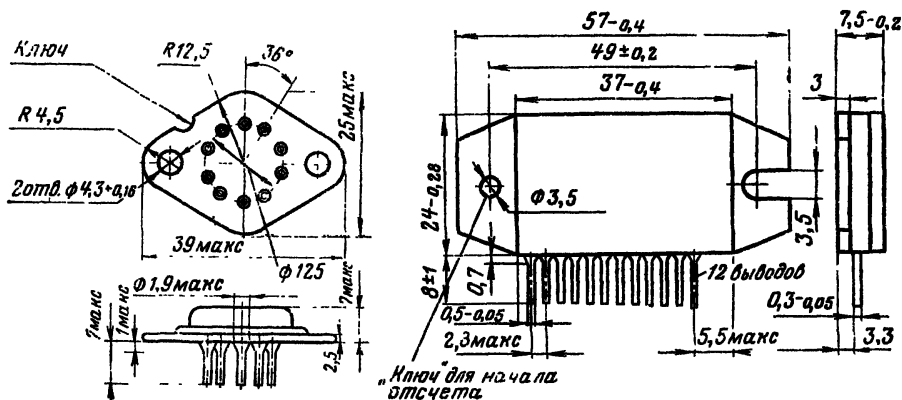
Корпус типа 311.10-1. Рис. 1-14. Корпус типа 422.12-1.
